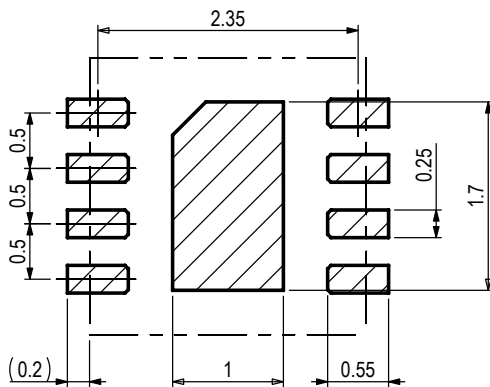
显示了陆地格局。土地模式被理解为PCB上的开放金属区域，DFN焊盘焊接在其上。
